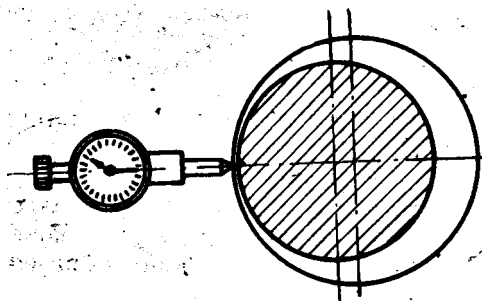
Схема начальной установки индикатора на измерение биения заготовки
